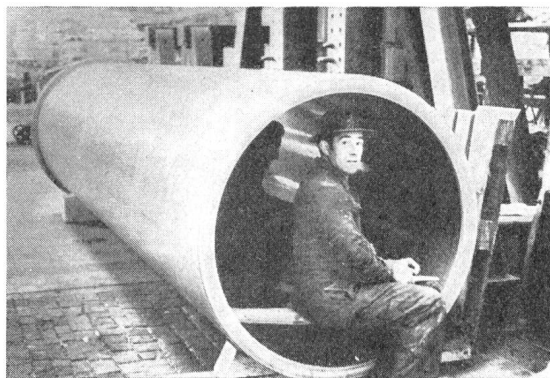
Luftspaltzylinder eines grossen wassergekühlten Generators
